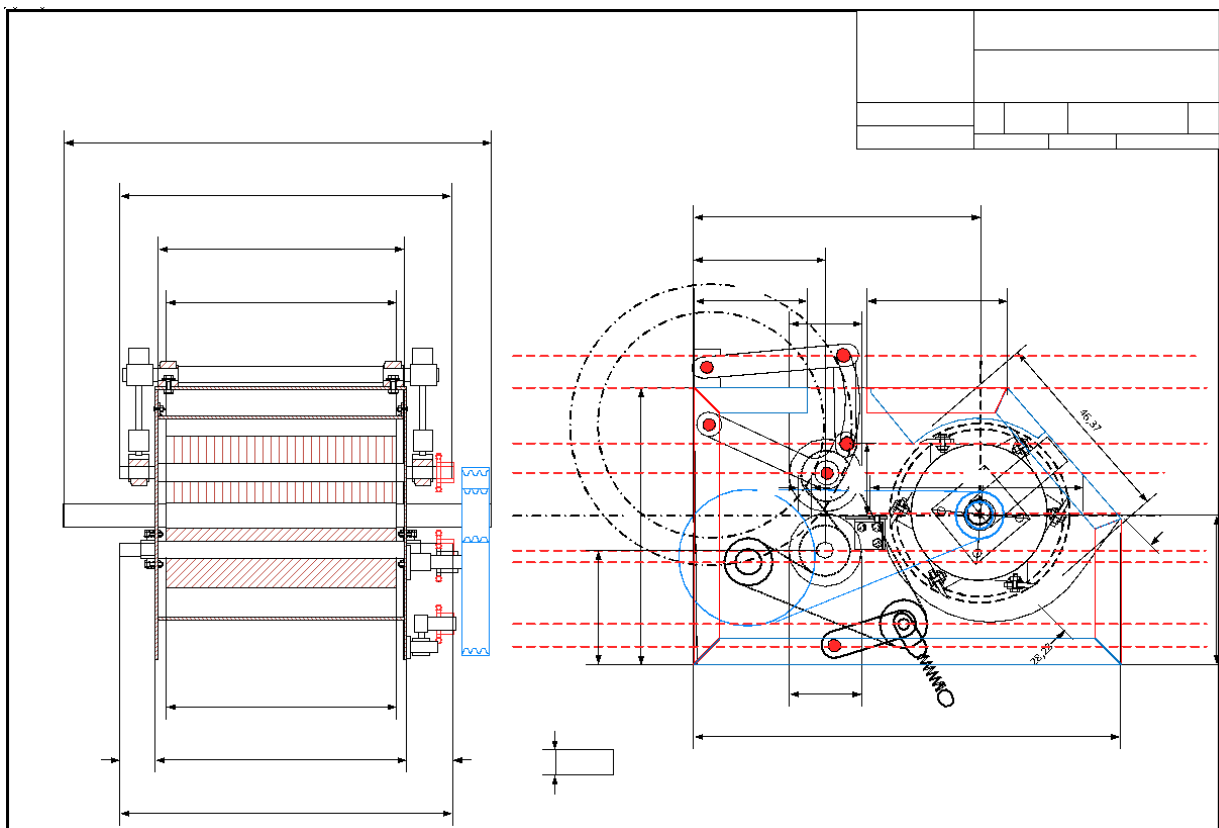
Rakitan bagian mesin pencacah dan motor penggerak
